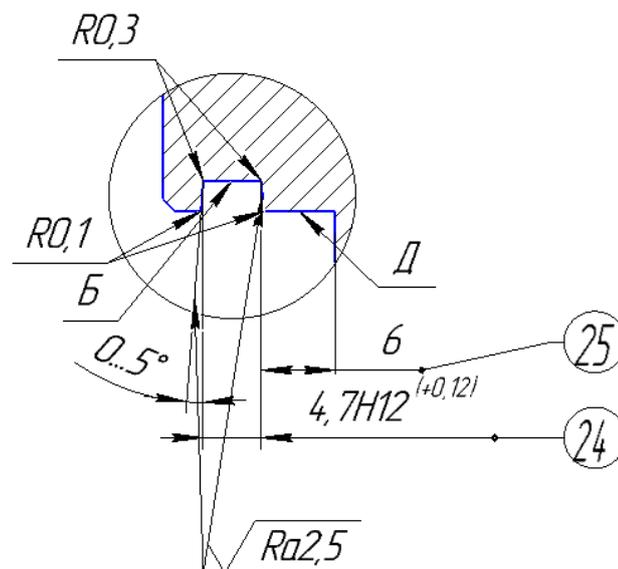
Вид К по чертежу. Нумерование поверхностей детали
